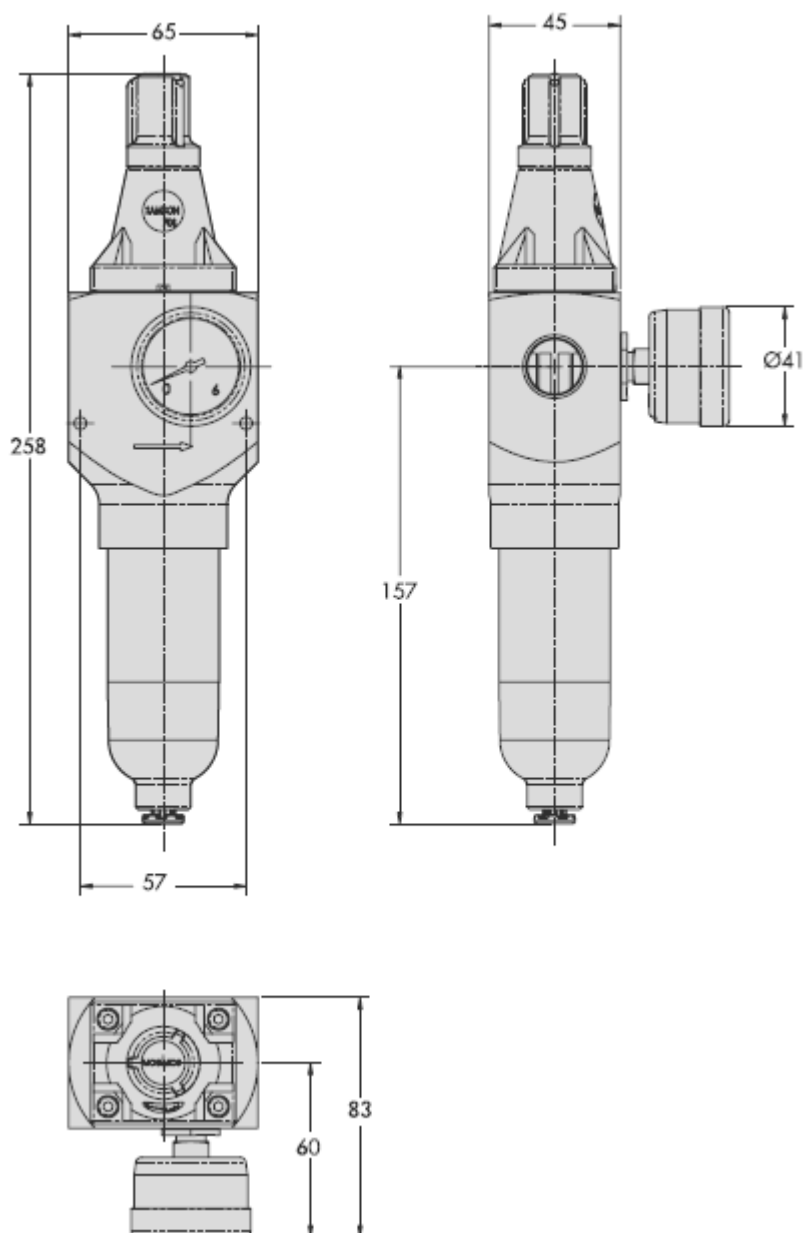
· Габаритный чертеж регулятора типа 4708-45
